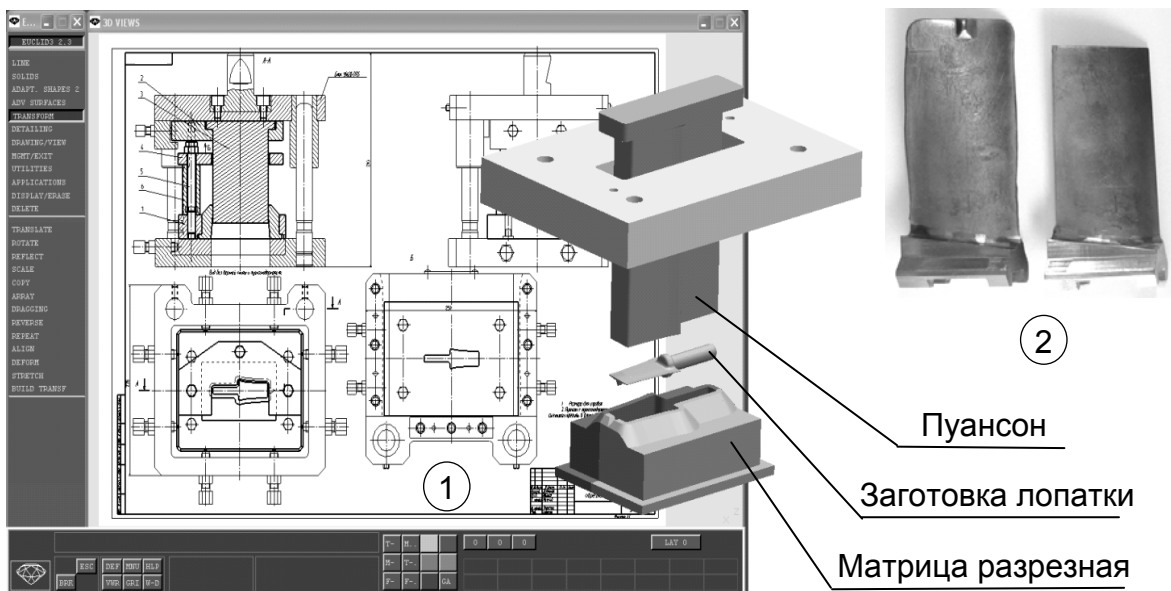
Обсечка обля: 1 – аналитические эталоны формообразующих деталей и чертеж обрезного штампа; 2 – фото заготовки лопатки компрессора до и после обсечки обля.
